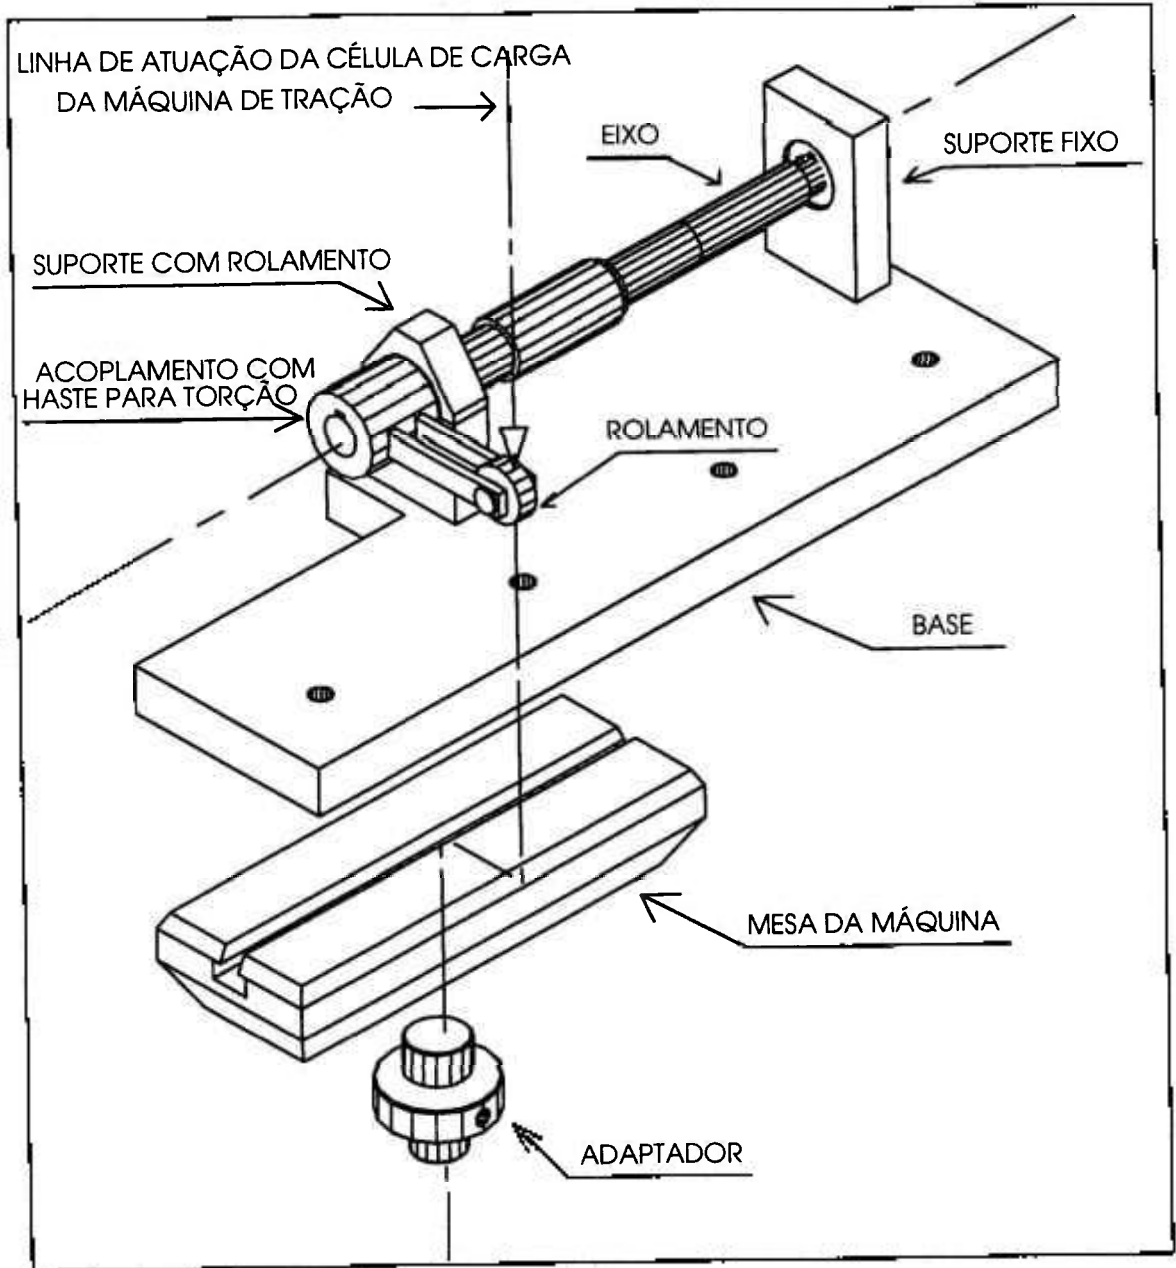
Arranjo do dispositivo para crescimento das trincas de fadiga
